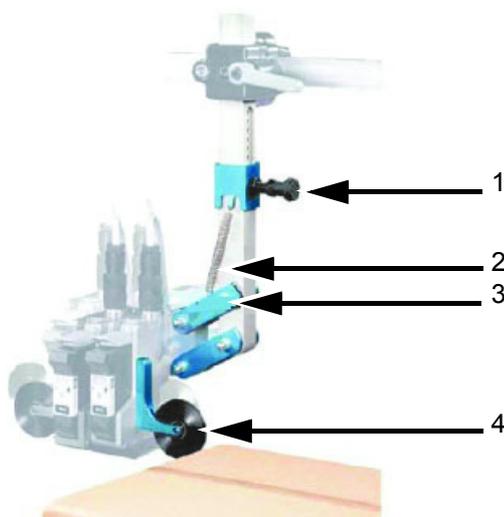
Крепёжный переходник из нержавеющей стали - золотистая печатающая головка
